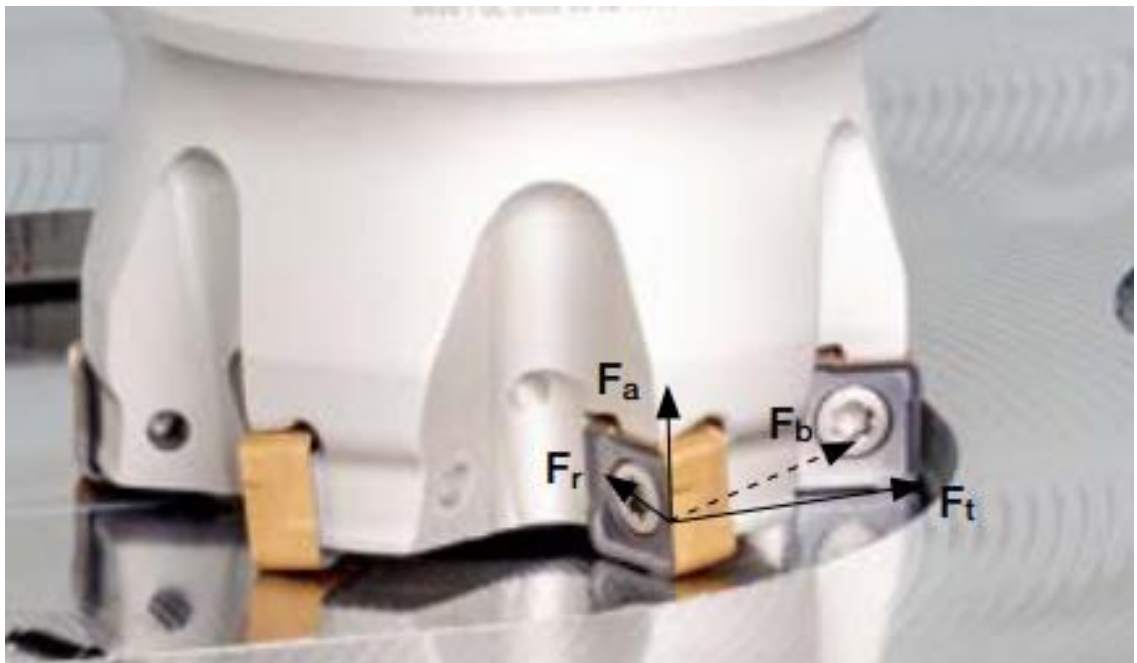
Схема просторової системи сил під час операції торцевого фрезерування
